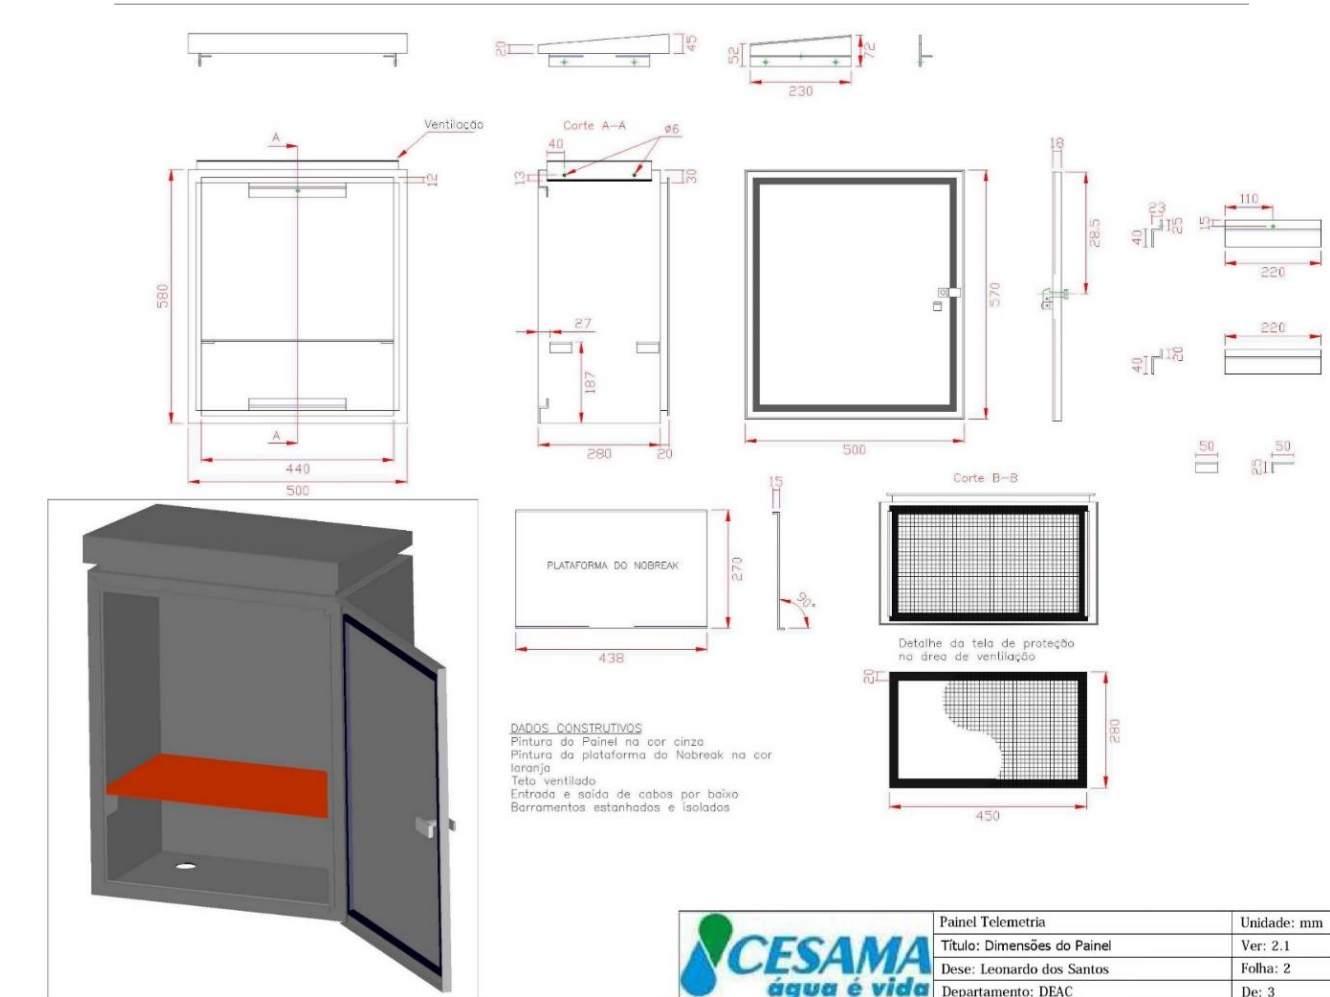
Detalhes construtivos painel de telemetria padrão CESAMA
